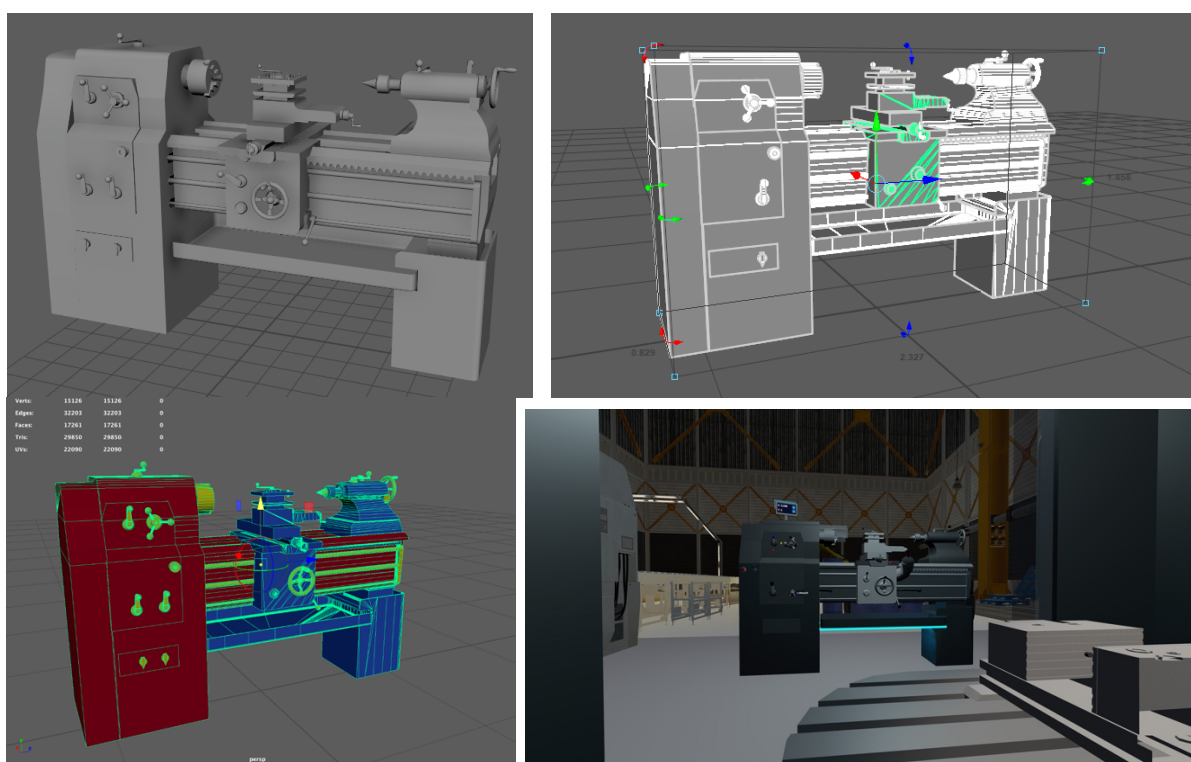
Детализированная модель токарного станка и окружение
